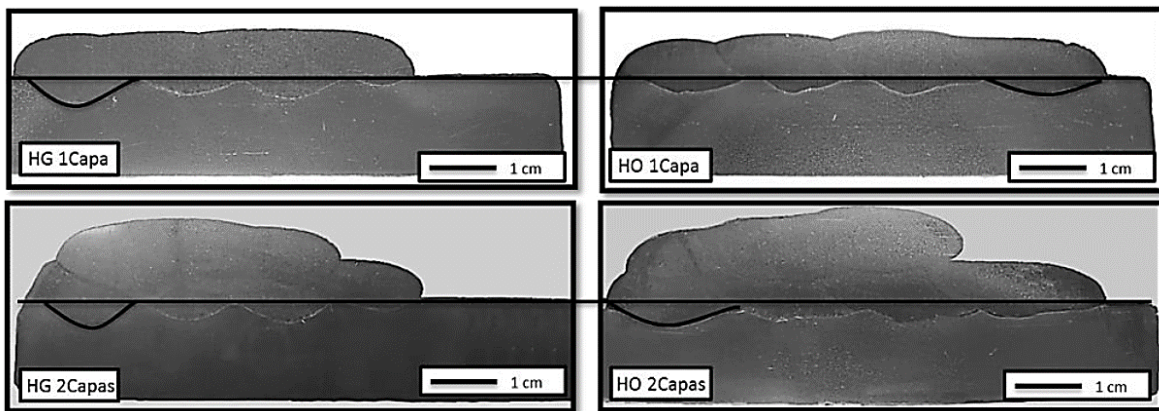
Macrografía de cortes transversales de los cupones soldados.
